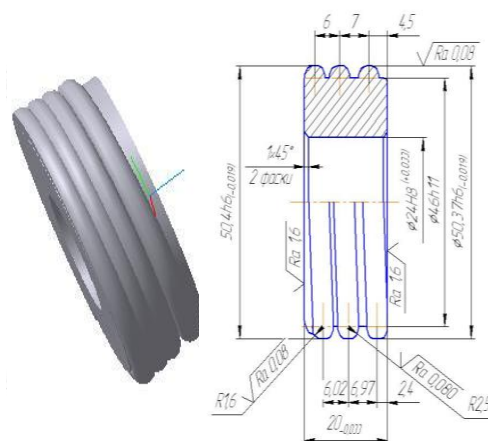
Тороїдальний ролик з гвинтоподібною робочою поверхнею
